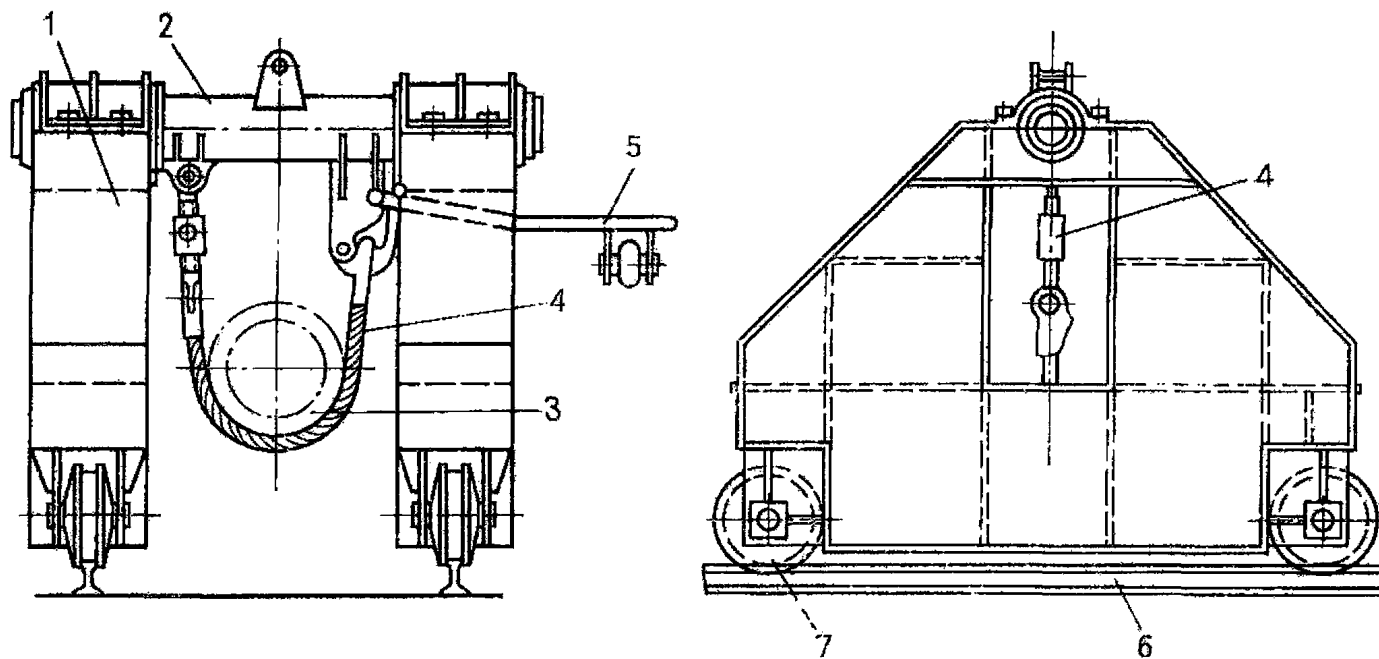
Конструкция тележки из комплекта оборудования для спуска трубопроводов ОСД-2:
